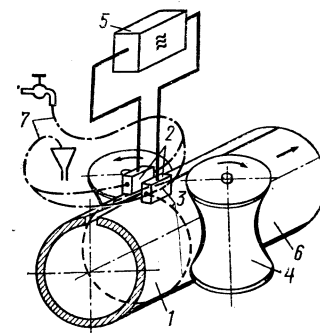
Сварка токами высокой частоты с контактными электродами:
